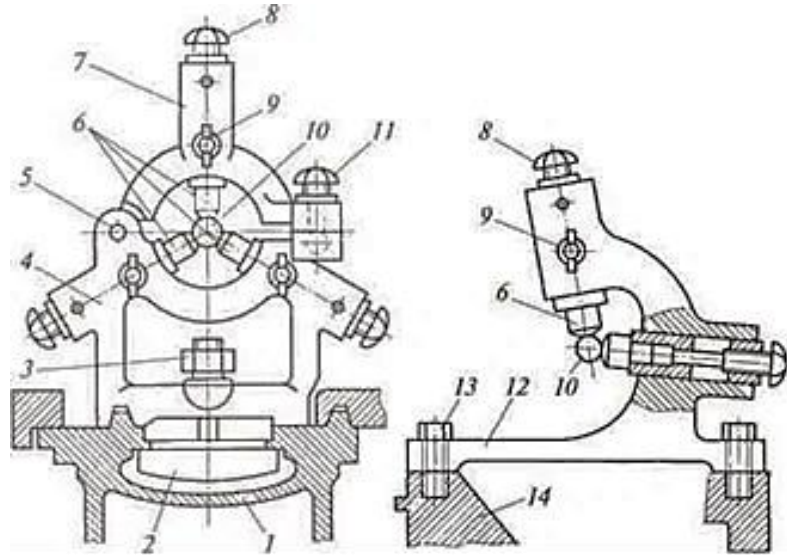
Люнети (нерухомий та рухомий) (1 – станина, 2 – притискач, 3 – гайка притискача, 4 – корпус, 5 – шарнір верхньої кришки, 6 – кулачки, 7 – кришка, 8 – гвинт регулювання, 9 – фіксатор кулачка, 10 – заготовка, 11 – фіксатор кришки, 12 – корпус, 13 – болт кріплення, 14 – повздовжній супорт)
